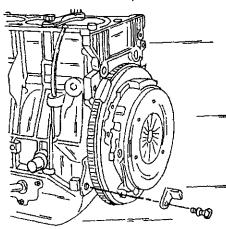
Применение стопора для блокировки маховика при отворачивании сцепления, маховика и ременного шкива коленчатого вала.
